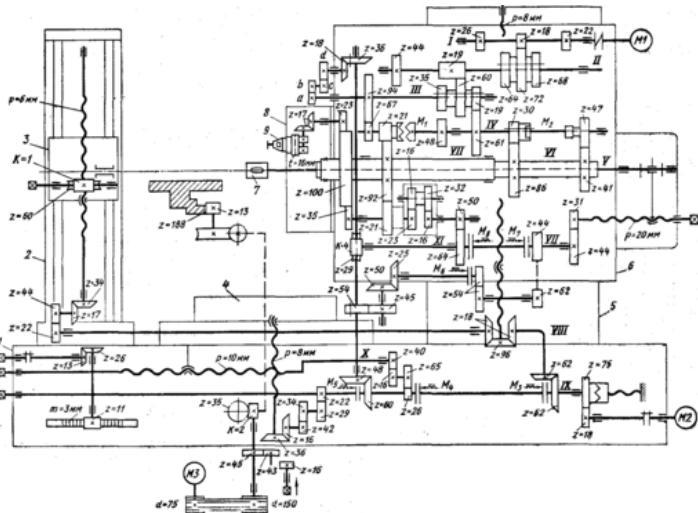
Схема горизонтально-расточного станка модели 262Г
